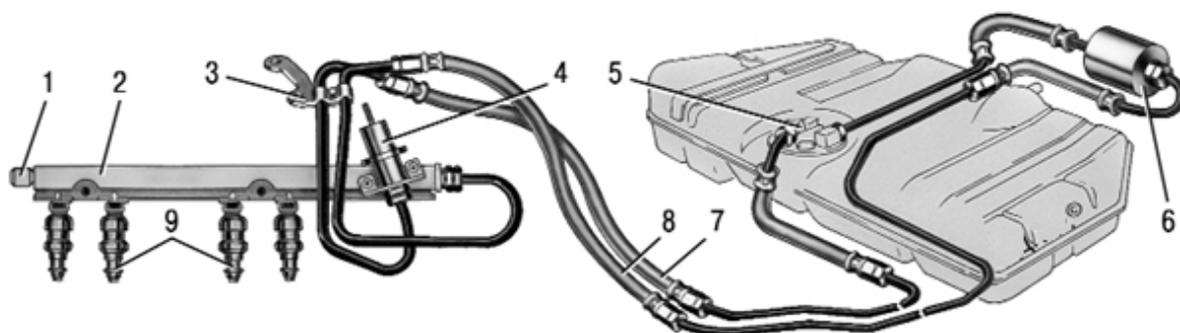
Система подачи топлива. 1 – пробка штуцера для контроля давления топлива; 2 – рампа форсунок; 3 – скоба крепления топливных трубок; 4 – регулятор давления топлива; 5 – топливный насос; 6 – топливный фильтр; 7 – сливной топливопровод; 8 – подающий топливопровод; 9 – форсунки
